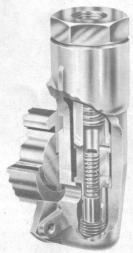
Coupe du couvercle de pompe montrant la soupape régulatrice de pression
